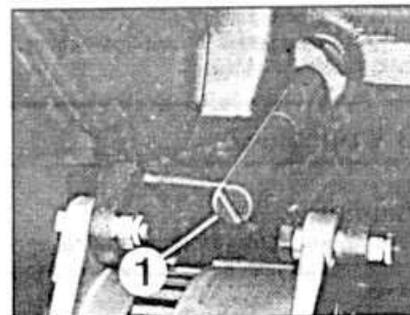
E.13. Оправка для установки коленчатого вала в положение ВМТ, установленная в блоке цилиндров двигателя.
